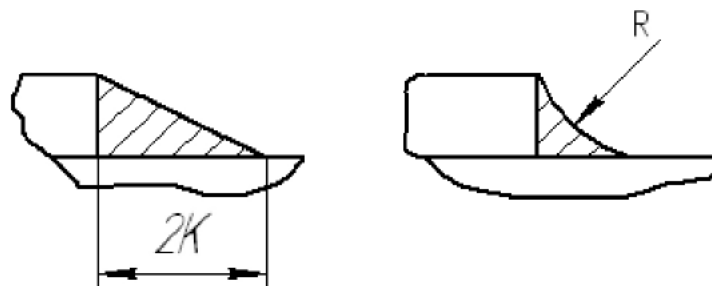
Валиковые сварные швы улучшенного профиля
